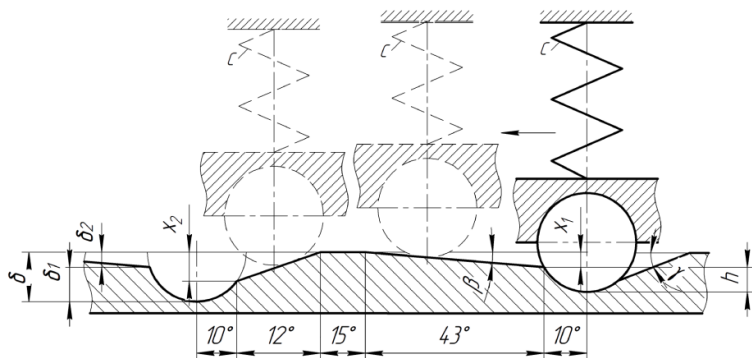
Схема розгортки робочої поверхні ведучої півмуфти
